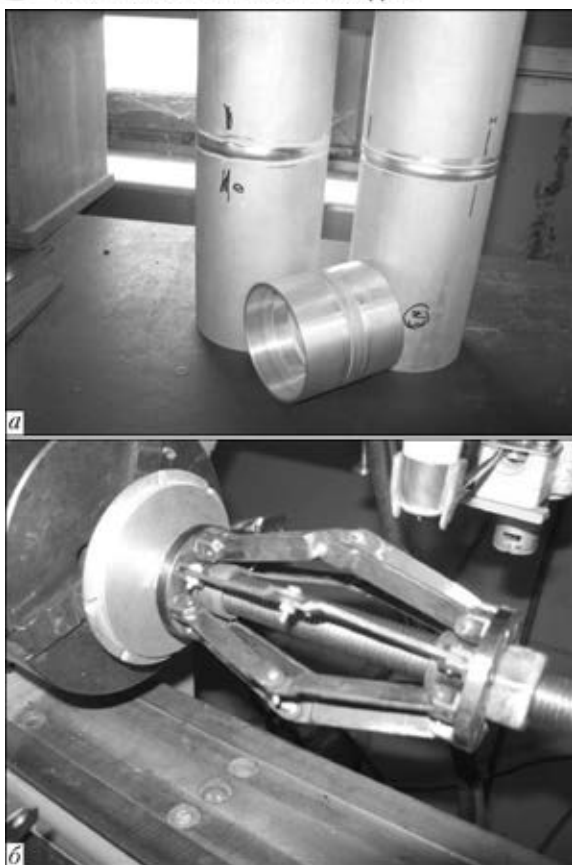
Общий вид образцов кольцевых стыков из сплава АМгб (а) и сборочное устройство для их сварки (б) (справа — нагружающая гайка)
